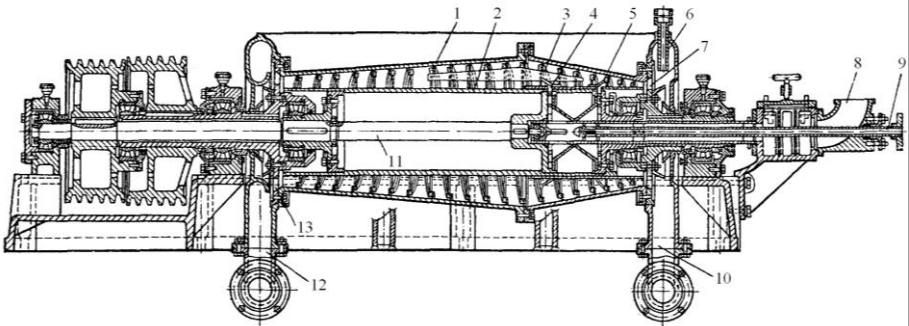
Схема відстійної центрифуги типу НОГШ із шнековим вивантажуванням осаду: 1 – ротор; 2 – барабан; 3 – шнек; 4 – живильний пристрій; 5 – пристрій впуску промивної води; 6 – труба; 7 – вікно вивантаження осаду; 8 – труба; 9 – живильна труба; 10 – приймальник осаду; 11 – горизонтальний вал; 12 – приймальник освітленої рідини; 13 – зливні вікна
